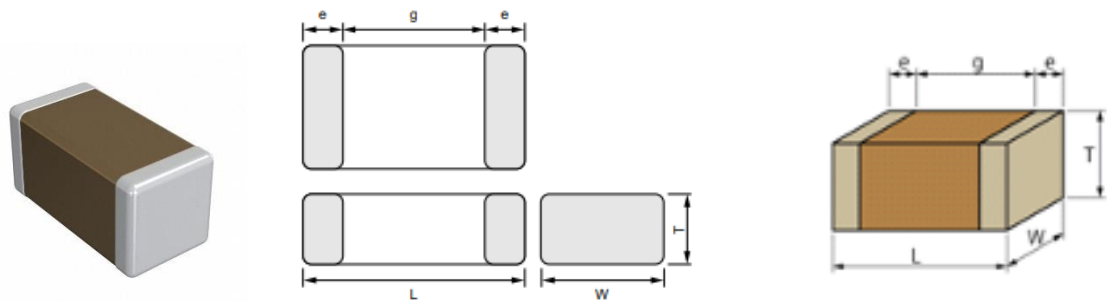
Зовнішній вигляд і розміри корпусу конденсатора GRM188R71H [10, 11]
